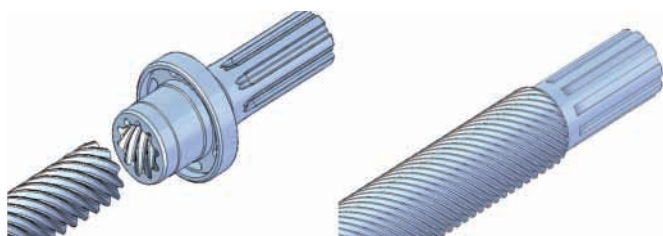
Сравнение нового конца вала редуктора с эвольвентным зацеплением (слева) и прежнего конструктивного исполнения для передачи усилия (справа, без конца вала редуктора)
